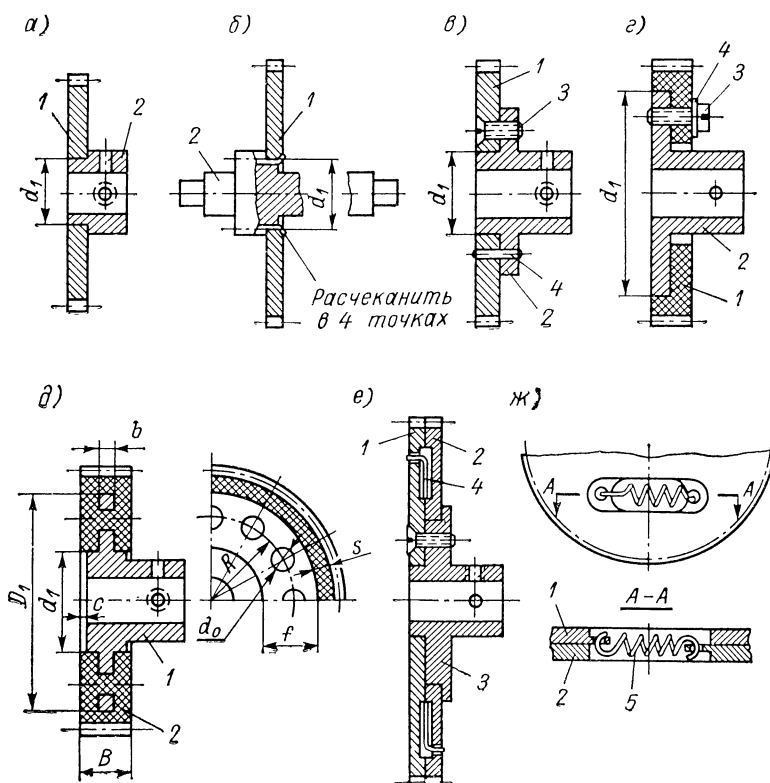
Сборные конструкции цилиндрических зубчатых колес
